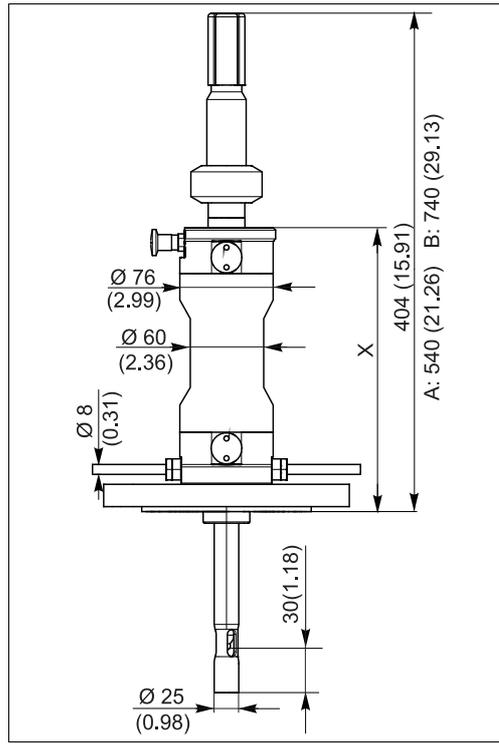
Ausführung: Standard, für Gel-Sensoren. Abmessungen in mm (inch)
